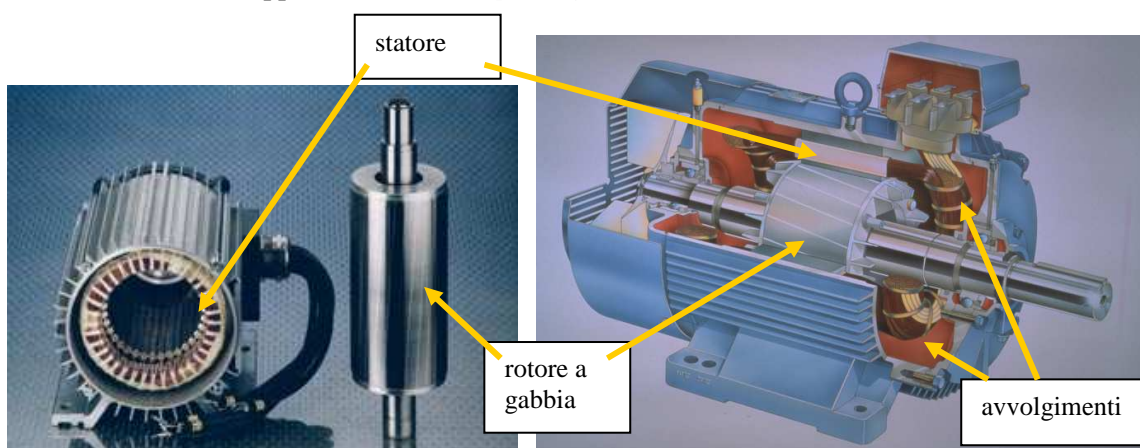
(a) Motore asincrono disassemblato (b) Spaccato di un motore asincrono
